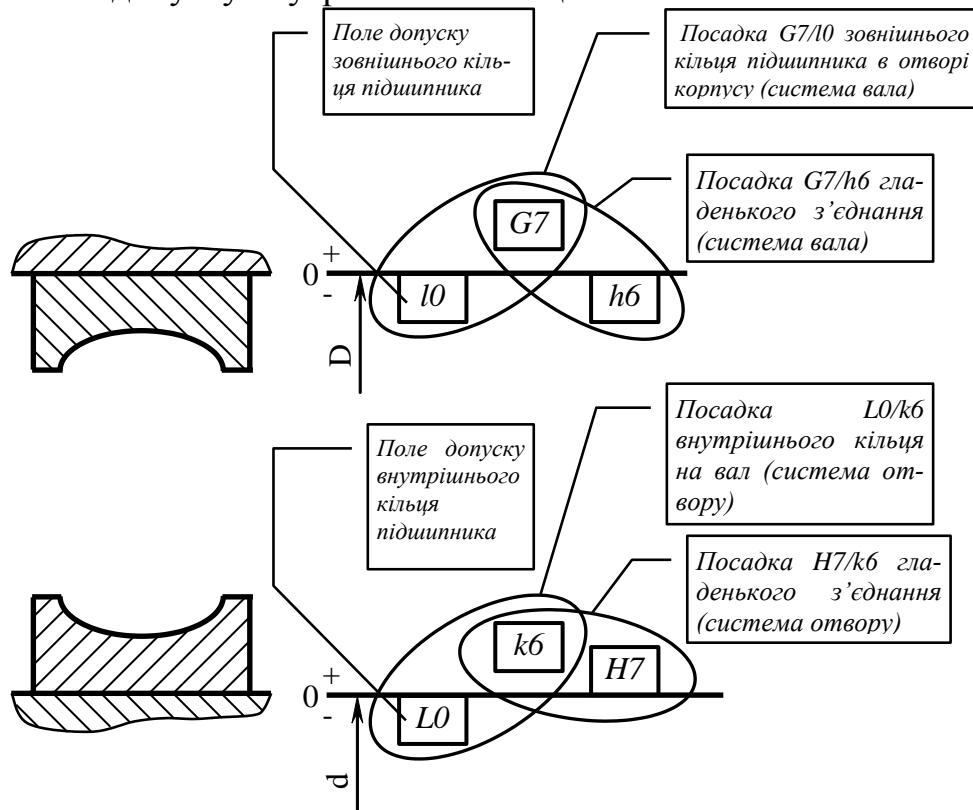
Порівняльна схема розташування полів допусків у з'єднаннях кілець підшипників і гладеньких циліндричних з'єднань
